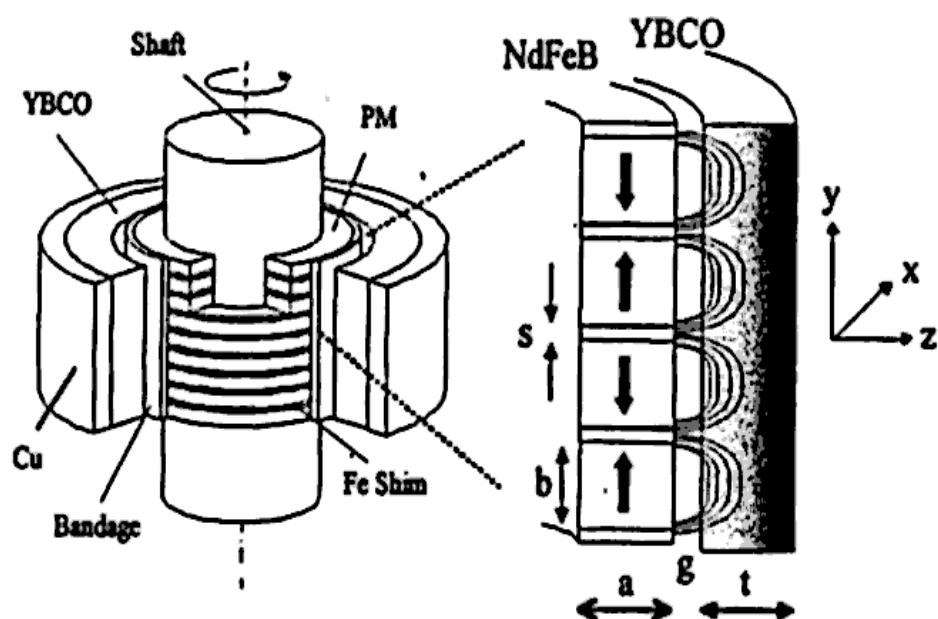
Конструкция ВТСП подшипника фирмы Siemens
